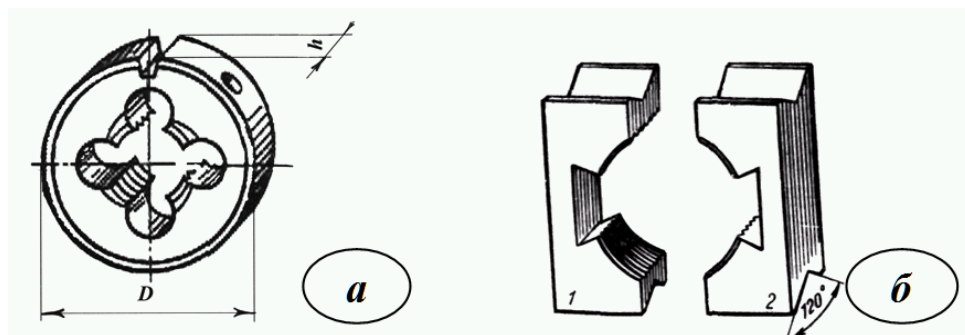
Плашки: а – кругла; б – розсувна.
